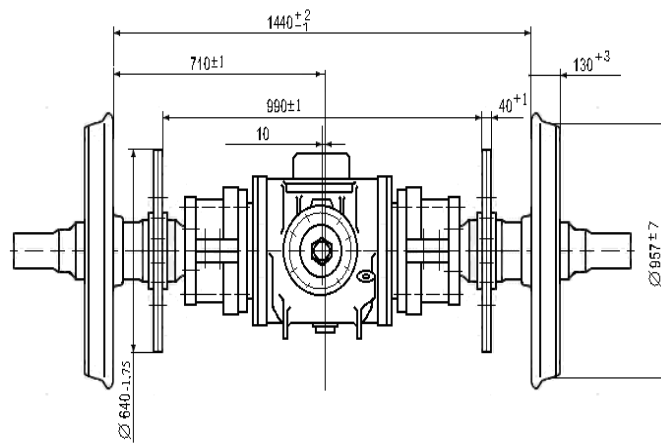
Колесная пара 4096.10.010 СБ с тормозными дисками ОАО «ТВЗ» и редуктором
